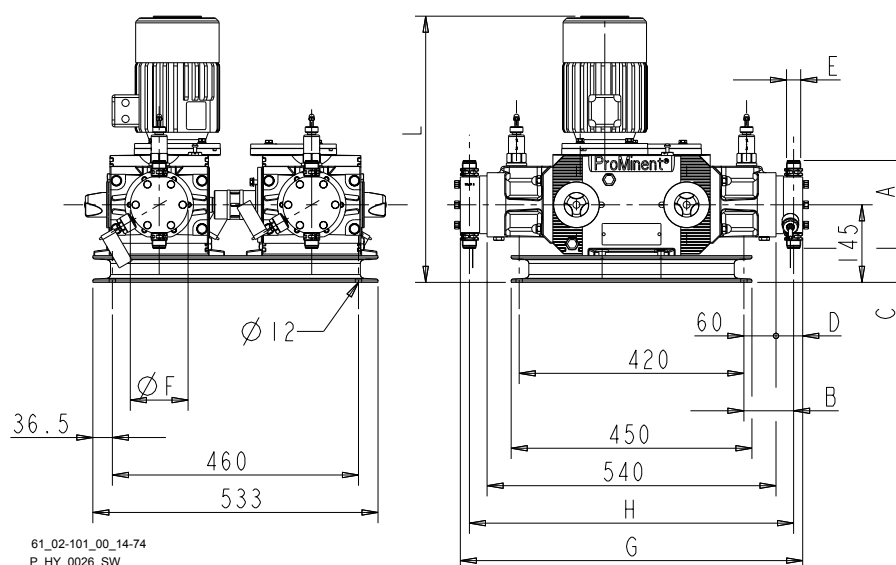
Hoja de dimensiones Hydro HP3 con accionamiento montado, modelos de cabezal doble (HP3a F + HP3a B) - Dimensiones en mm
